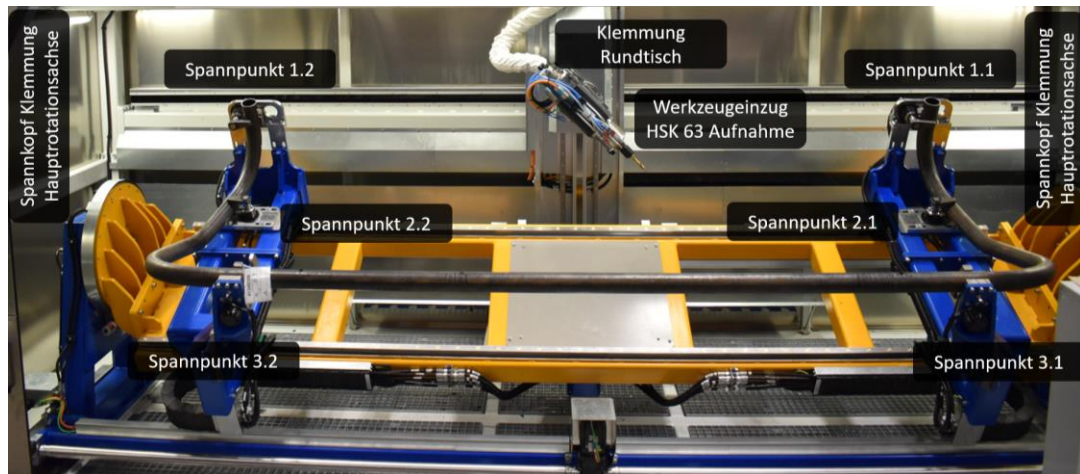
Gesamtübersicht Hydraulikkomponenten Bohrautomat
